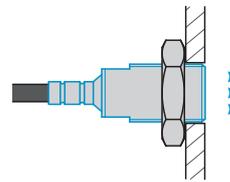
Flächenbündige Montage eines geschirmten Sensors in einer metallischen Halterung
